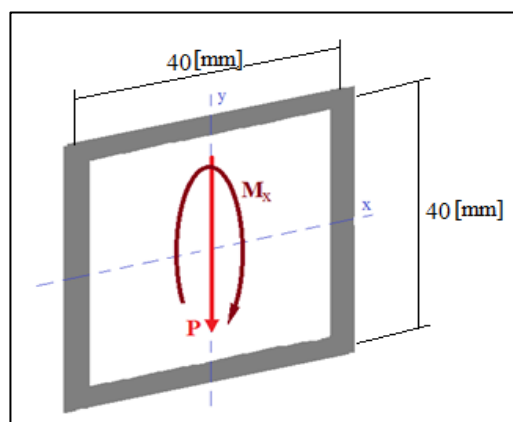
Fuerzas y momentos en la unión soldada en la junta superior.
